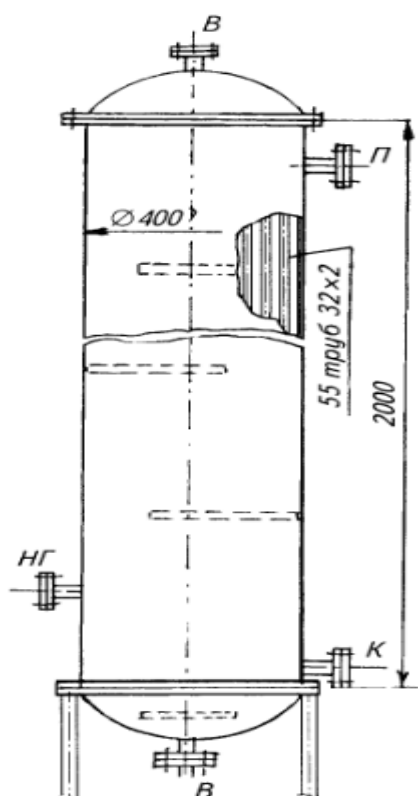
Вертикальный кожухотрубный конденсатор:
